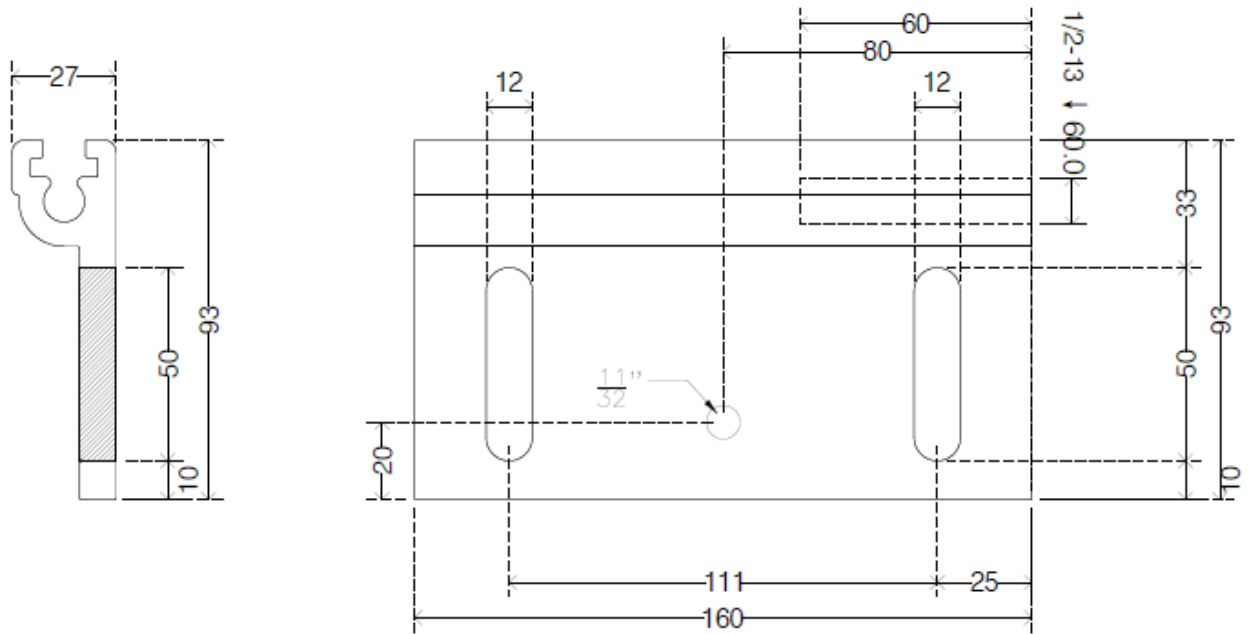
Detalle ancla hembra perfil 70456. Fuente Aluvisa (2019)
